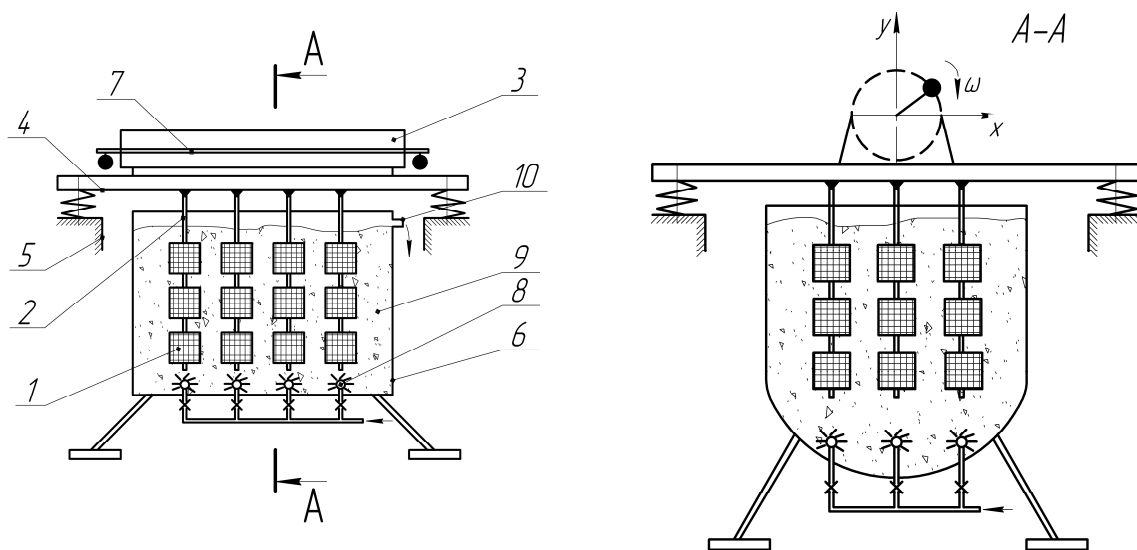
Схема новой разновидности способа виброобработки: 1 – обрабатываемые детали; 2 – установочные пальцы; 3 – инерционный вибровозбудитель; 4 – колебательная система; 5 – жесткая опора; 6 – резервуар; 7 – вал; 8 – гидродинамические устройства; 9 – рабочая среда; 10 – отвод
